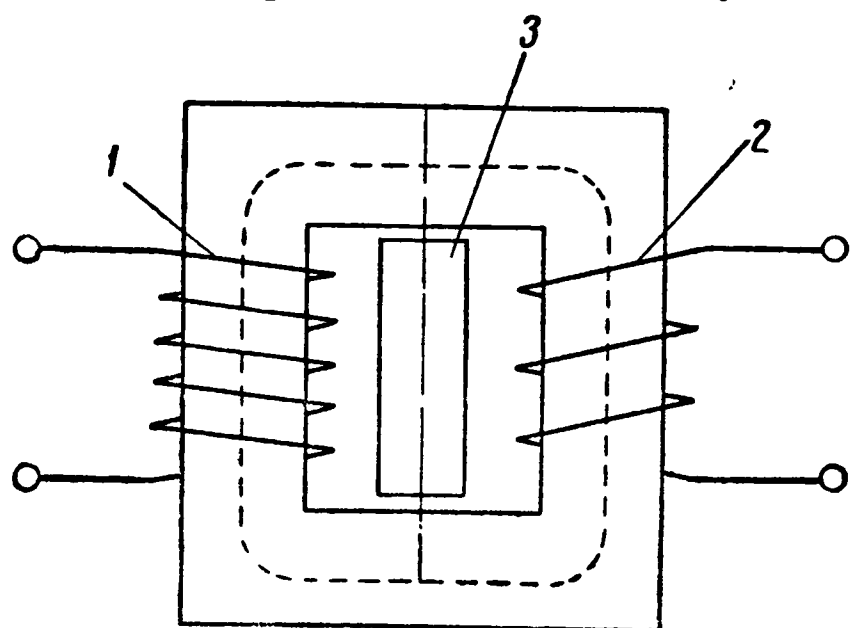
Схема сварочного трансформатора СТАН
